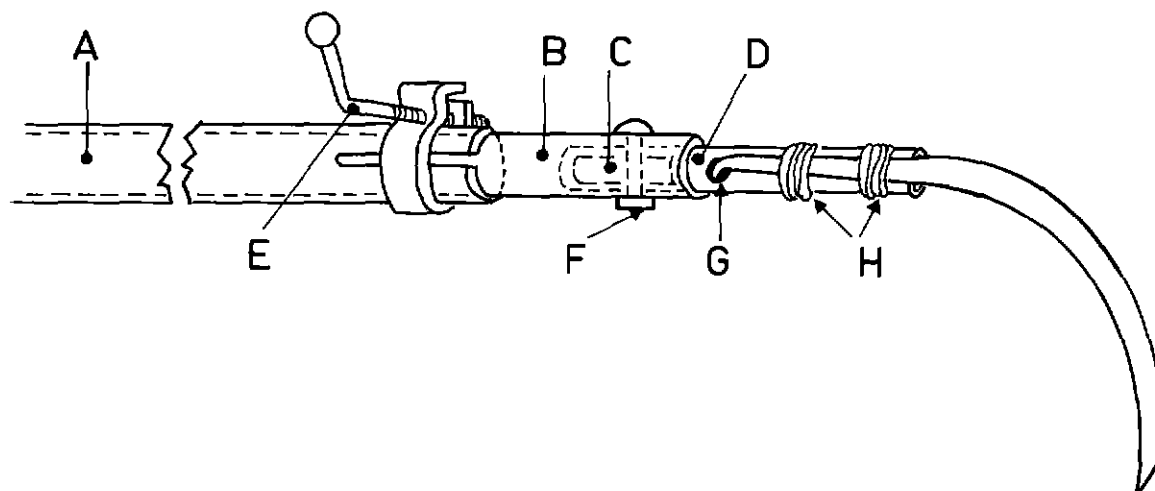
A : Tube extérieur en alliage d'aluminium (*Outer new aluminum tube - Tubo exterior de aleación de aluminio*) L = 6 m ;  $\varnothing$  ext. = 44 mm.
